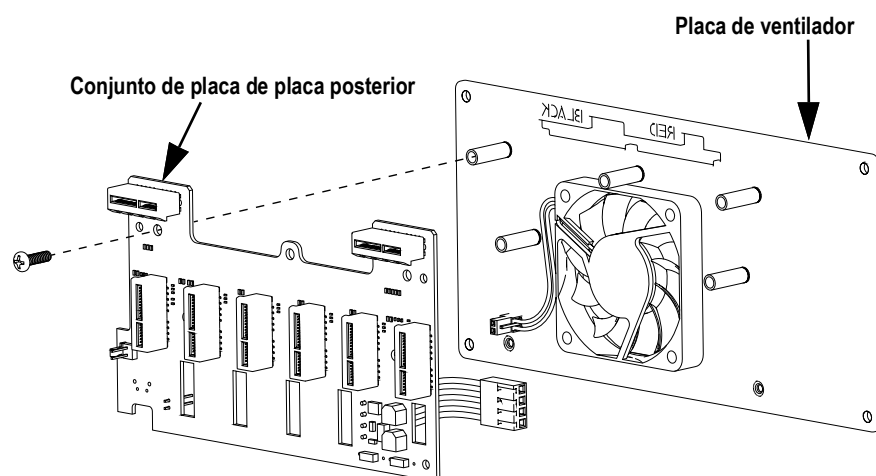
Desmontaje del conjunto de placa de placa posterior
